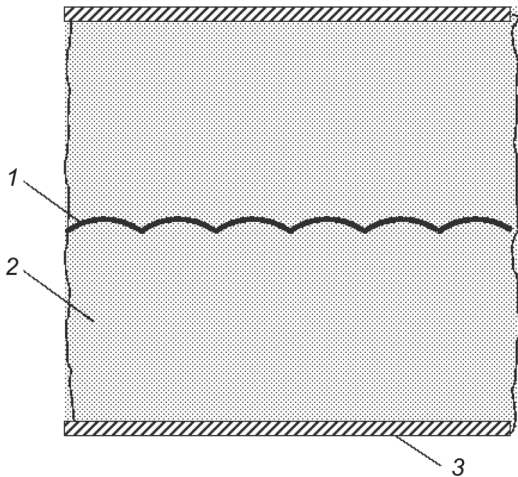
Схематическое изображение участка трубчатого электронагревателя в разрезе: 1 – нагревательный элемент; 2 – электроизоляционный наполнитель; 3 – трубчатая оболочка
